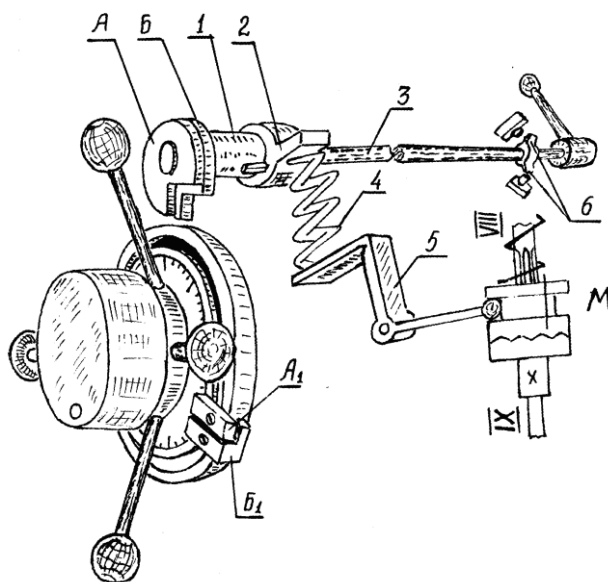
Схема механизма ограничения глубины сверления и реверса шпинделя станка.
